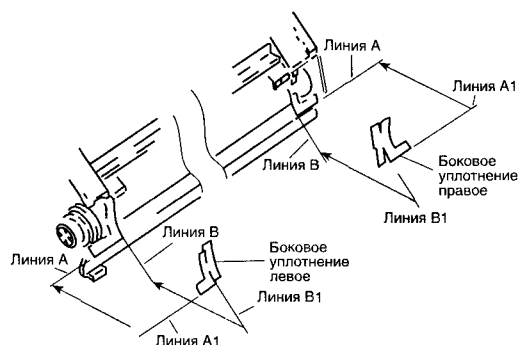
Крепеж боковых уплотнений магнитного ролика
